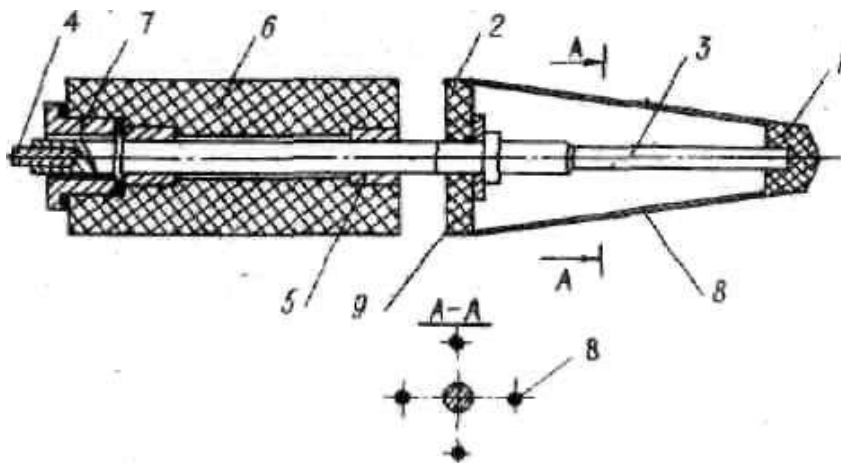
Устройство для съема ягод при ручном сборе: 1 – диск; 2 – диск; 3 – вал; 4 – гибкий валик; 5 – подшипник; 6 – ручка; 7 – гайка; 8 – эластичная нить; 9 – винтовой механизм
